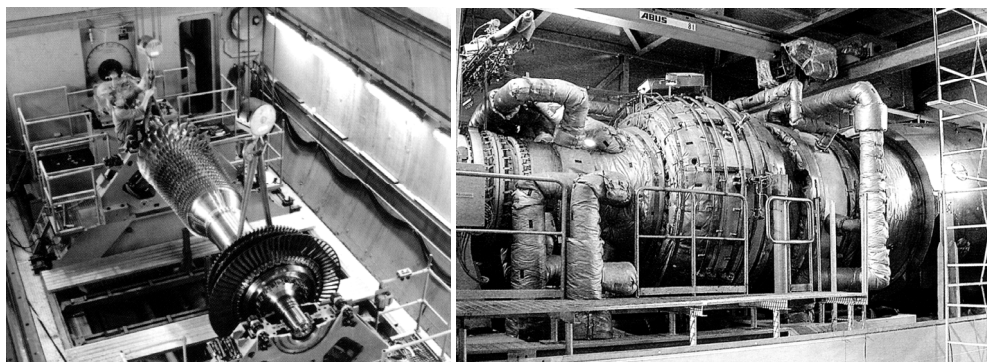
Общий вид и компоновка SGT-800 [41]:
